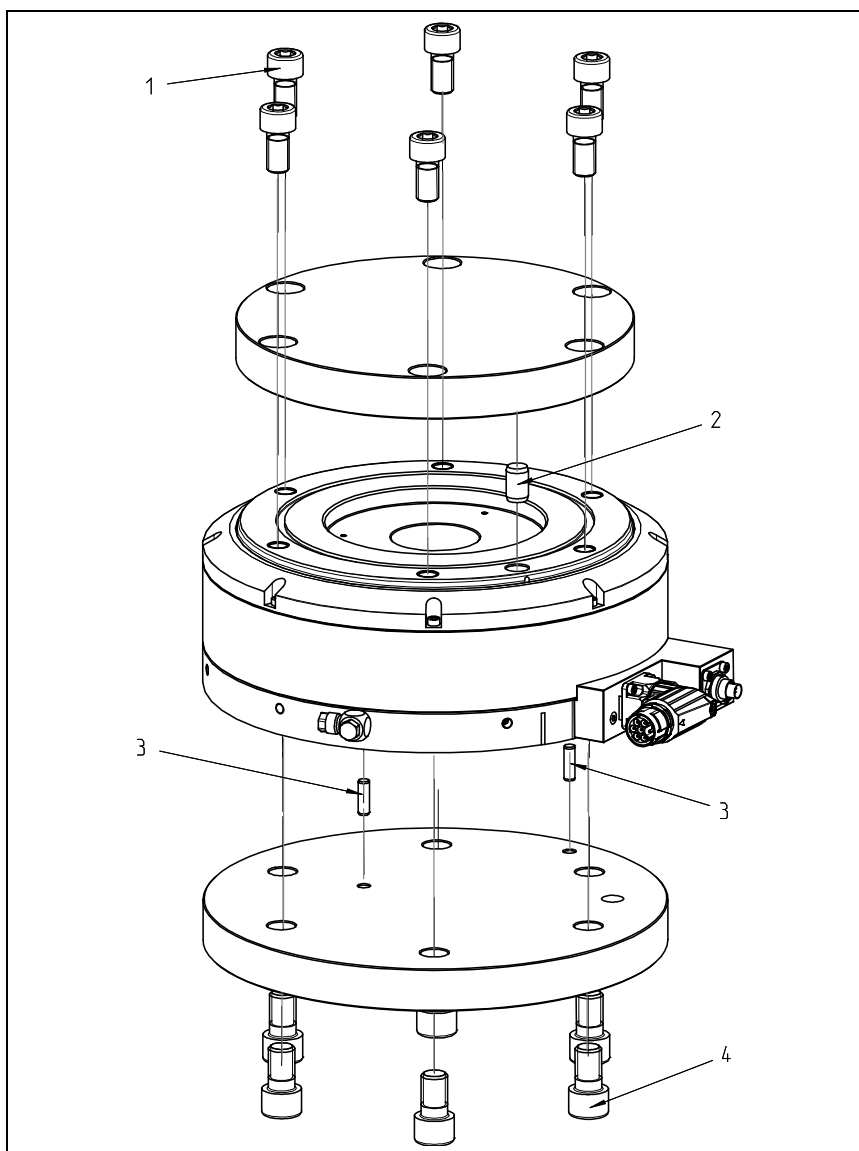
Ansicht Montage der Adapterplatten am Rotor und Grundträger
